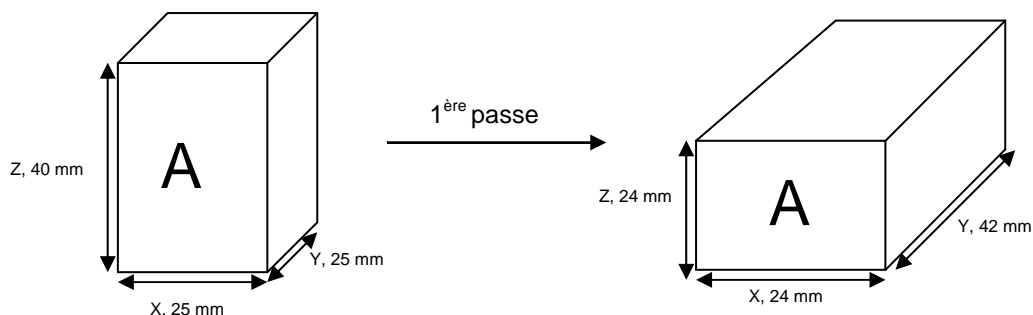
Géométries initiale et finale du lopin de la première passe des gammes de mini-forgeage I et A.
